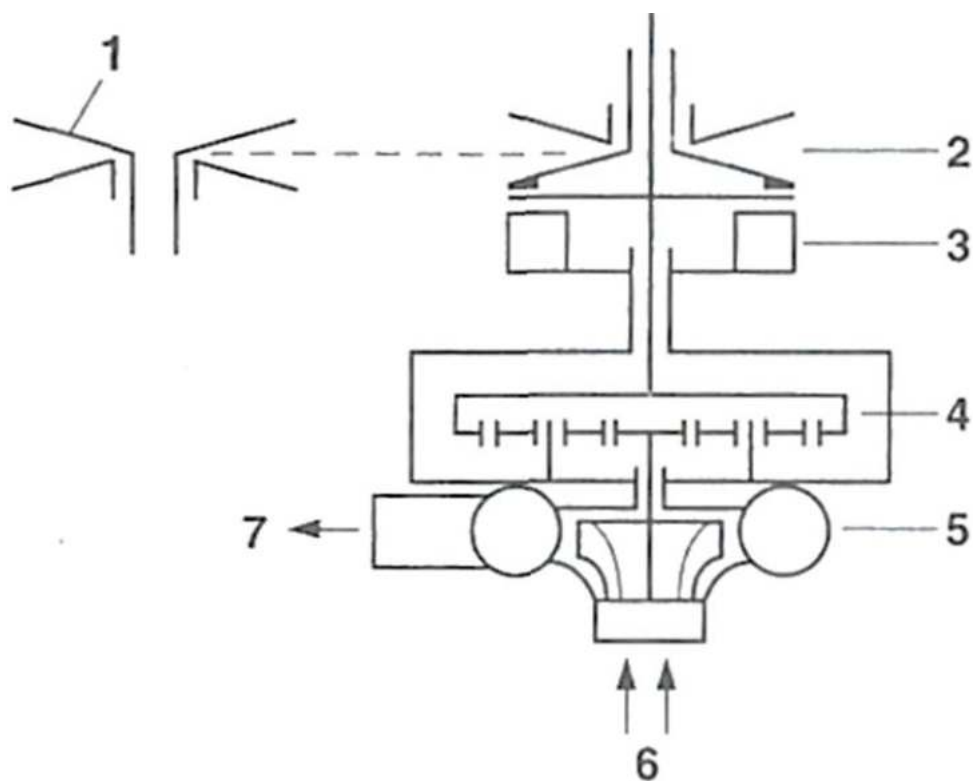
Устройство автомобильного центробежного компрессора
